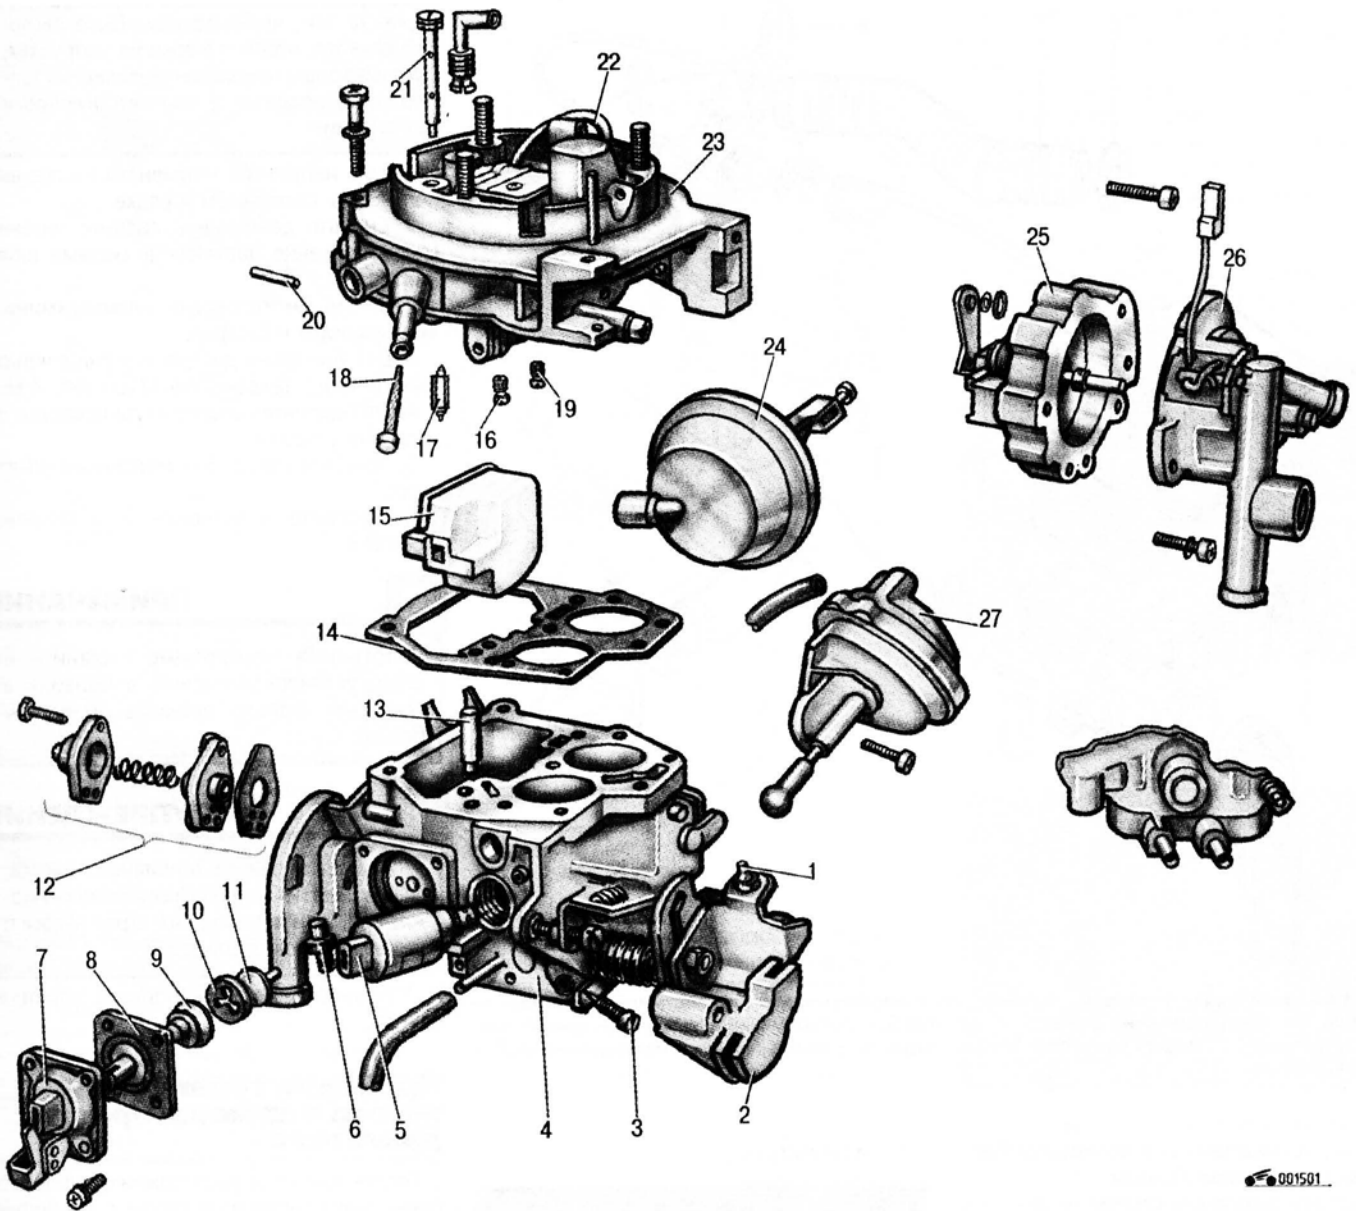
Устройство карбюратора Pierburg 2E3: 1 – винт регулировки приоткрытия дроссельной заслонки при пуске двигателя; 2 – сектор; 3 – винт регулировки качества (состава) смеси; 4 – корпус; 5 – электромагнитный клапан; 6 – упорный винт; 7 – крышка ускорительного насоса; 8 – диафрагма ускорительного насоса; 9 – пружина; 10 – седло клапана; 11 – клапан ускорительного насоса; 12 – экономайзер мощностных режимов; 13 – распылитель ускорительного насоса; 14 – прокладка крышки; 15 – поплавок; 16 – главный топливный жиклер первой камеры; 17 – игольчатый клапан; 18 – фильтр; 19 – главный топливный жиклер второй камеры; 20 – ось уплавка; 21 – жиклер холостого хода; 22 – трубка экономайзера; 23 – крышка; 24 – пневмопривод воздушной заслонки; 25 – автоматическое пусковое устройство; 26 – крышка пускового устройства; 27 – пневмопривод дроссельной заслонки второй камеры
